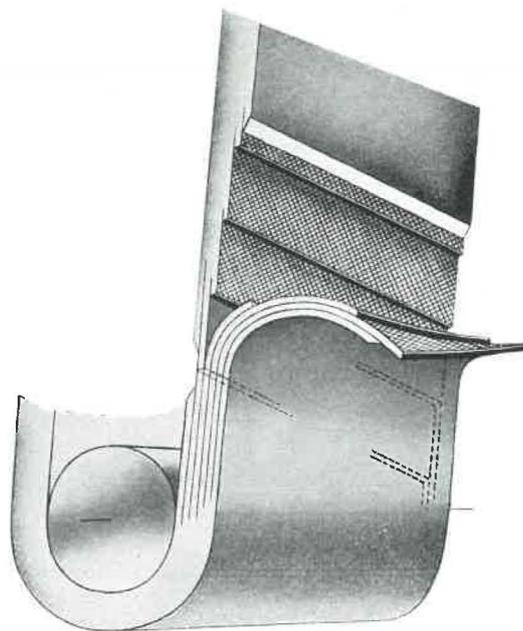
Découpe des extrémités de deux courroies qui doivent être soudées l'une à l'autre.
